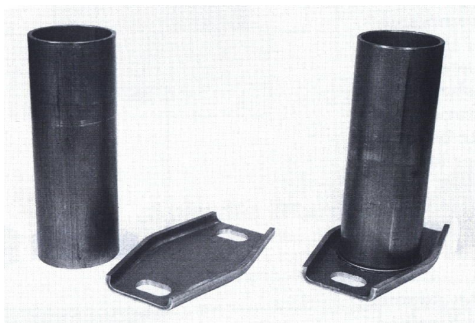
Partie d'un amortisseur: tube soudé à une pièce compressée [1].
